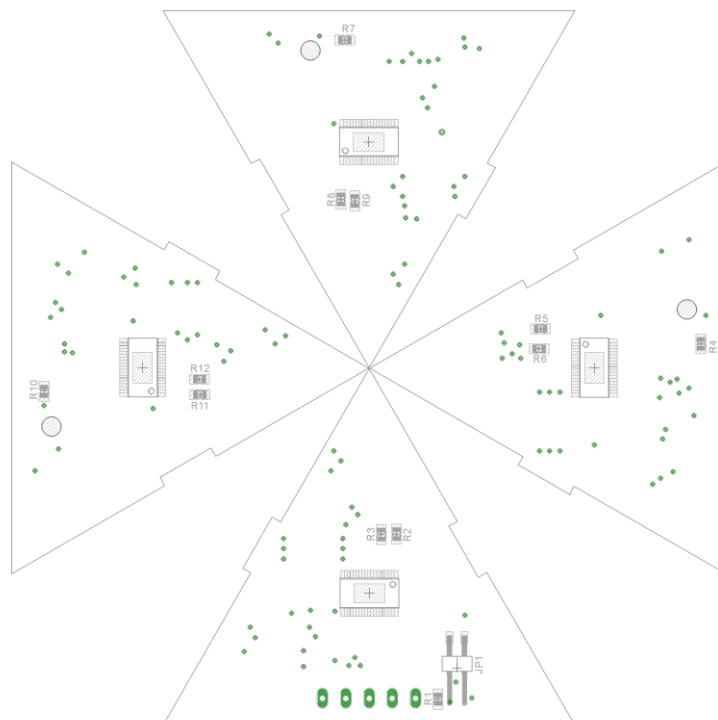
Bestückungsplan gespiegelt Bottom LightPCB
